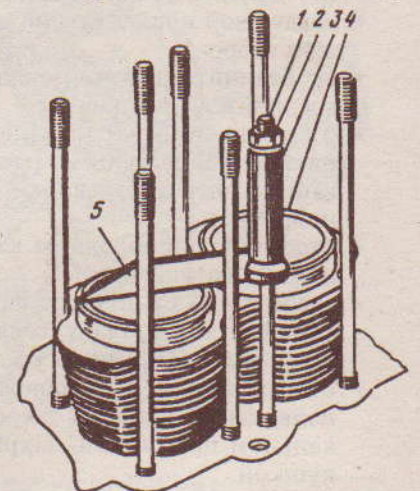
Приспособление для фиксации цилиндров на картере коленчатого вала: 1 – шпилька крепления головки цилиндров; 2 – гайка; 3 – фиксатор; 4 – цилиндр; 5 – прижимная планка
